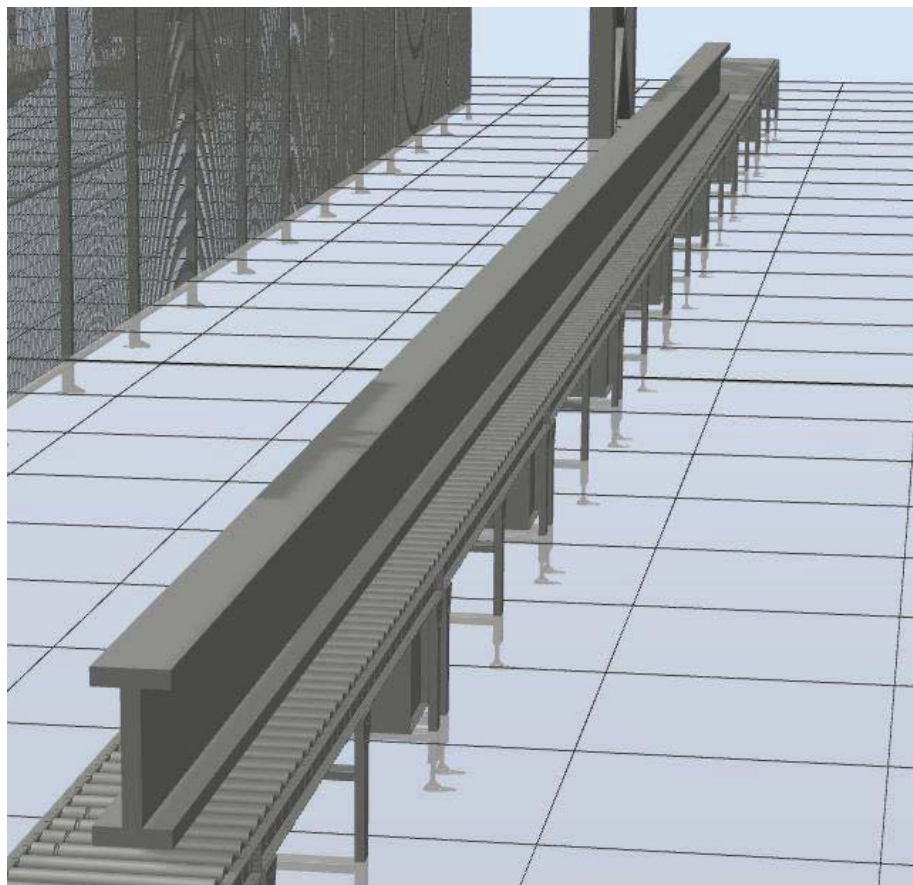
Reper tip grindă metalică de dimensiuni mari
